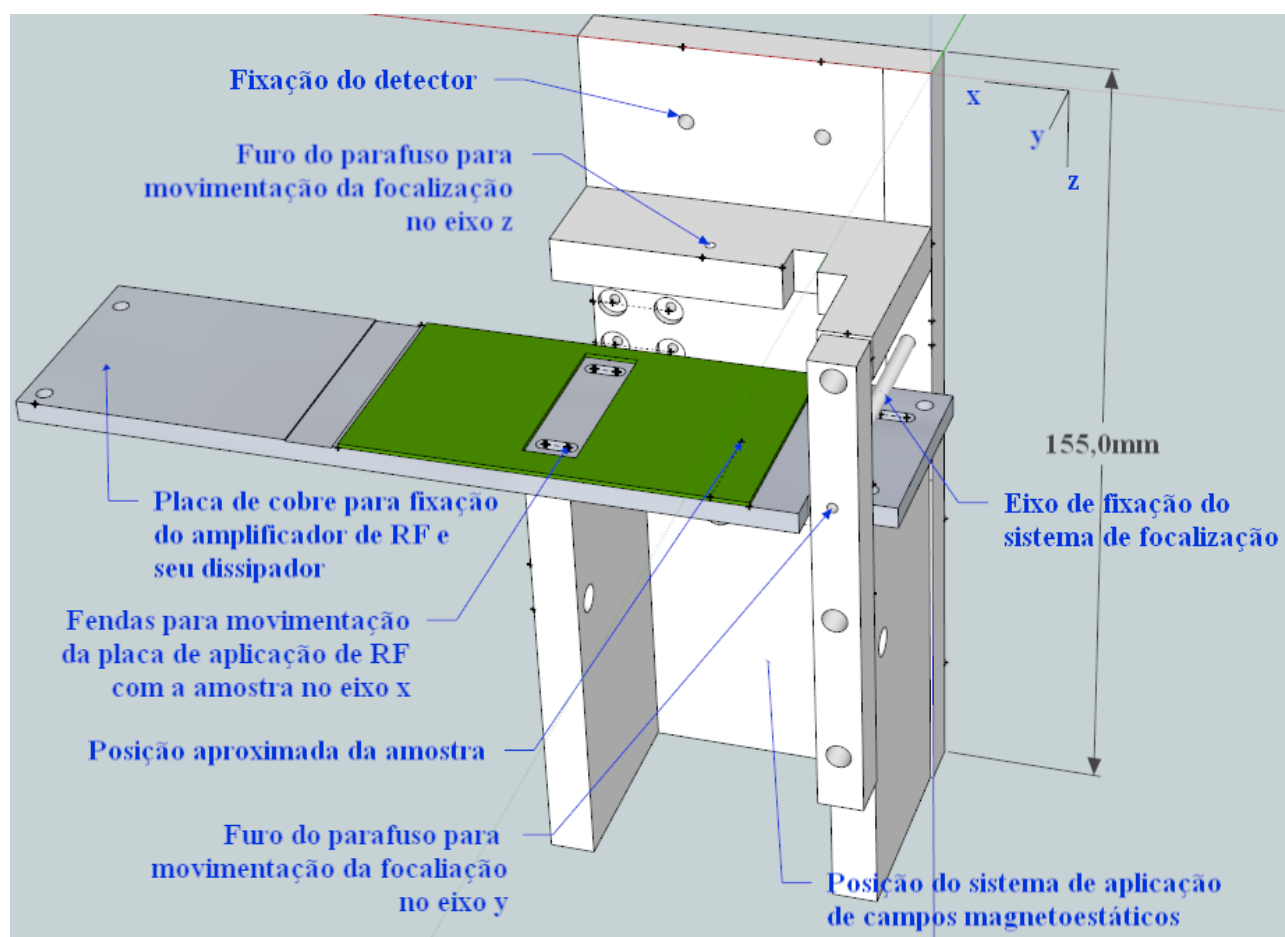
Partes principais da base de alumínio que une os diferentes componentes do sistema desenvolvido.
